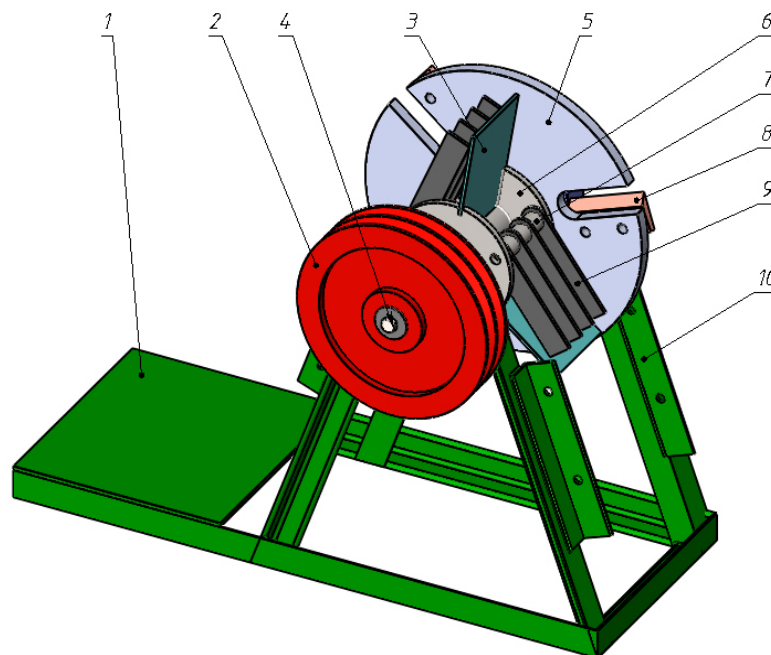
Монтажна схема машини для виготовлення деревної тріски
